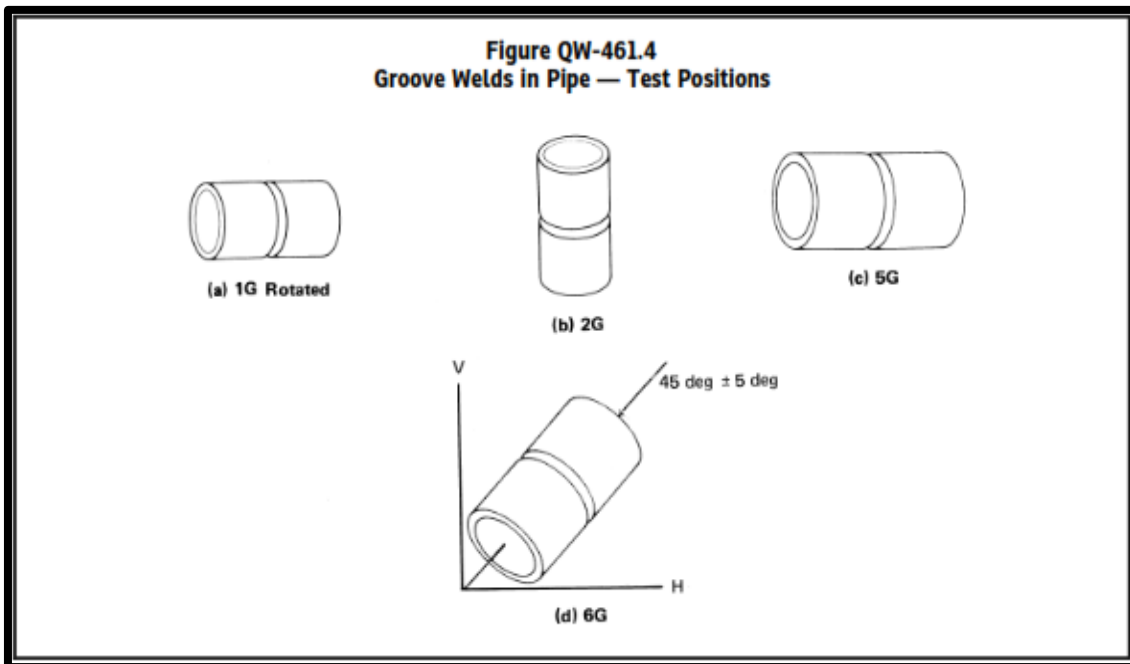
QW-461.4 Soldaduras de ranuras en tubos – posiciones de ensayos. Tomada del estándar ASME sección IX
